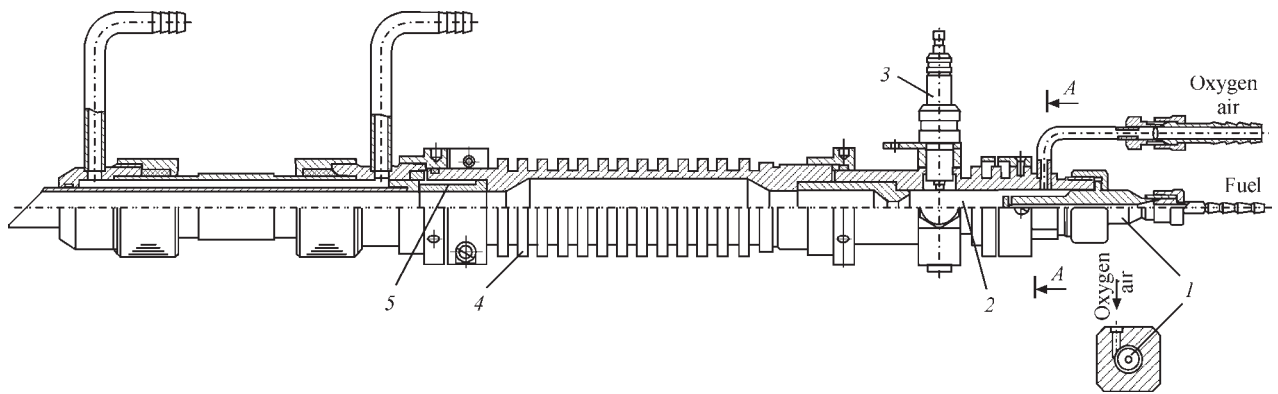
Безклапанний детонаційний пристрій з циліндричною форкамерою
